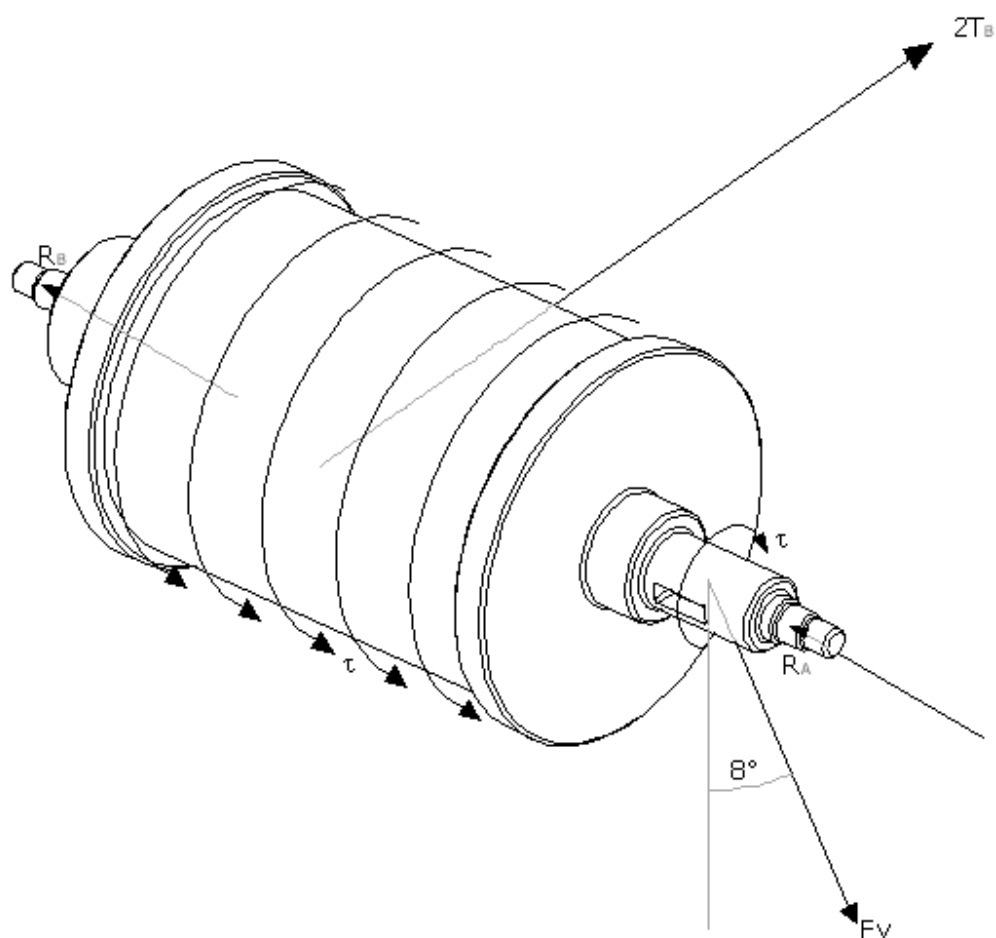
Esquema de las fuerzas actuantes sobre el rodillo motriz.
